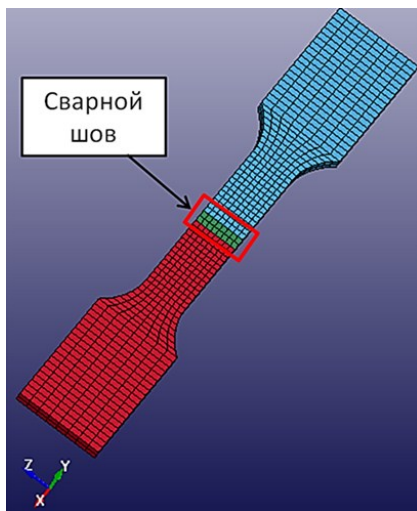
Модель сварного образца из сплава ВТ6ч.
